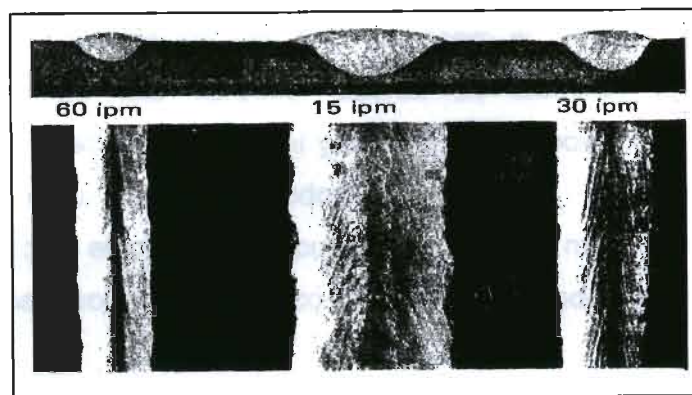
Efecto de la velocidad sobre las características de soldadura⁽⁴⁾.
